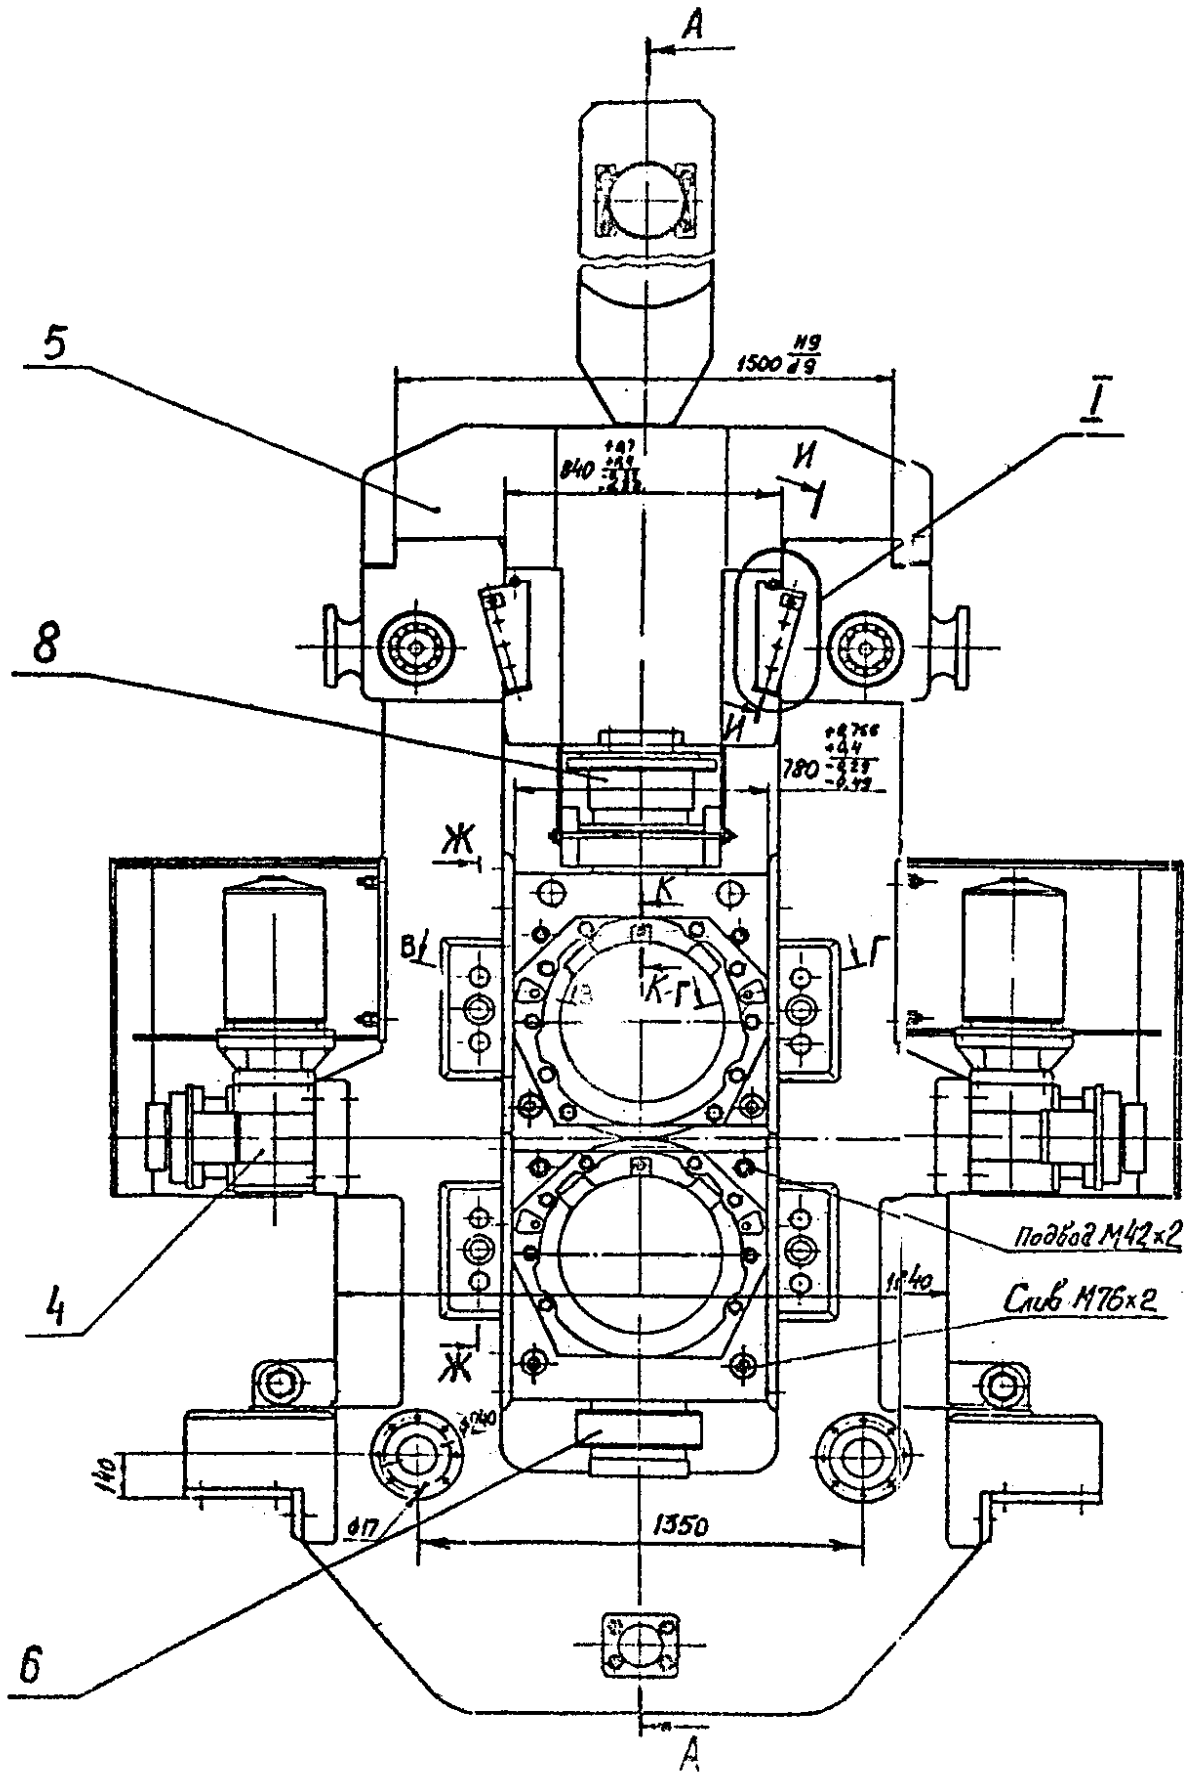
Кліть 730 . Загальний вид (вид збоку)
